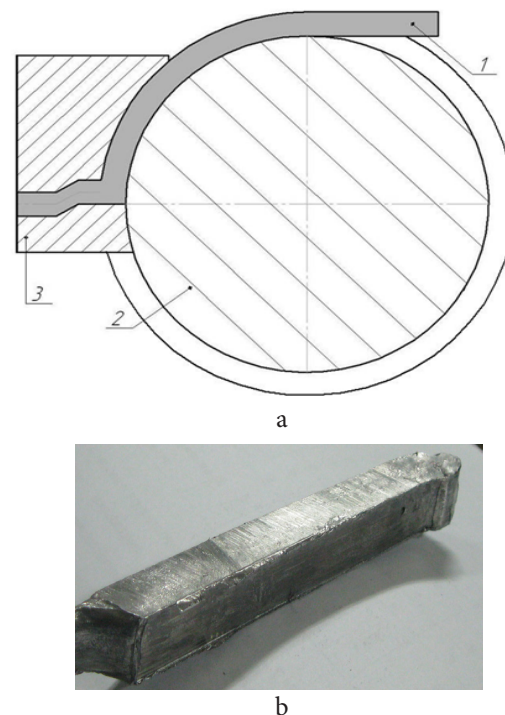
Схема процесса Мульти-РКУП-Конформ (а): 1- заготовка, 2-колесо, 3- матрица; заготовка после обработки методом Мульти-РКУП-Конформ (б).
